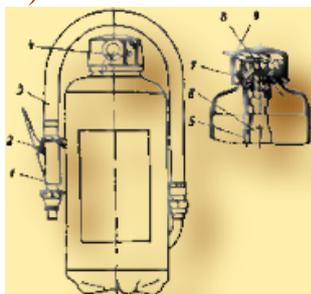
Общий вид ручного порошкового огнетушителя ОП-5:
